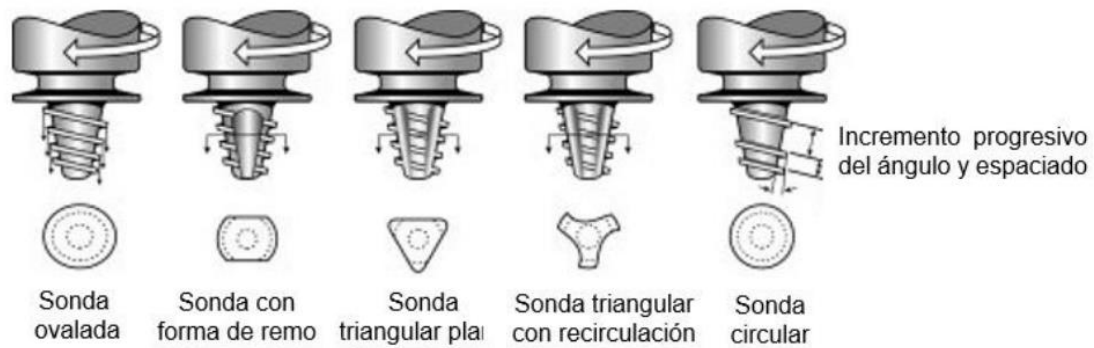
Tipos de Herramientas usadas en la soldadura por fricción-agitación [17].
